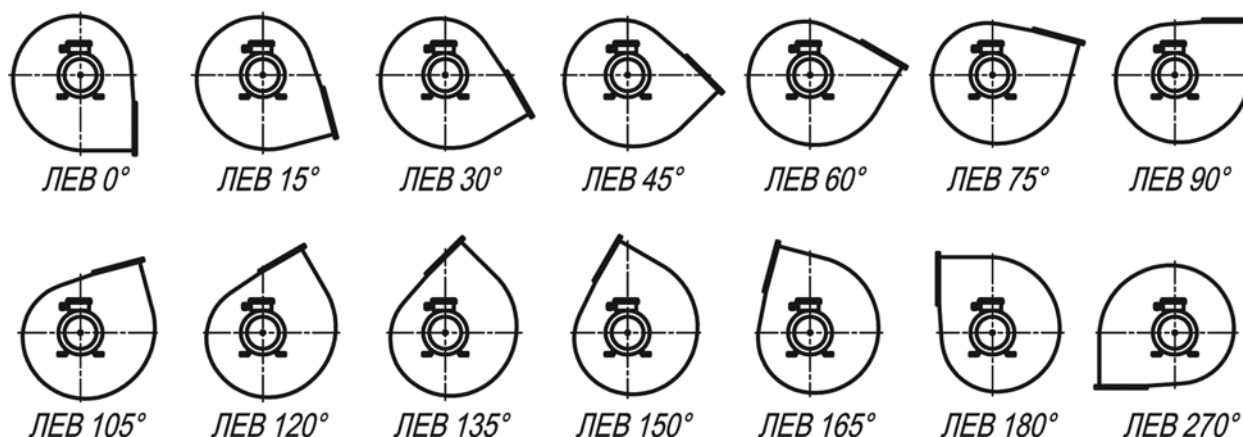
Положение корпуса тягодутьевых машин типа ВД и Д (ЛЕВ).
